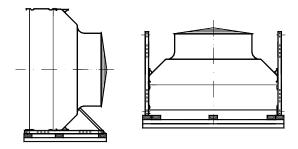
Izquierda: el equipo embalado sobre su costado. Derecha: equipo empacado en posición horizontal
